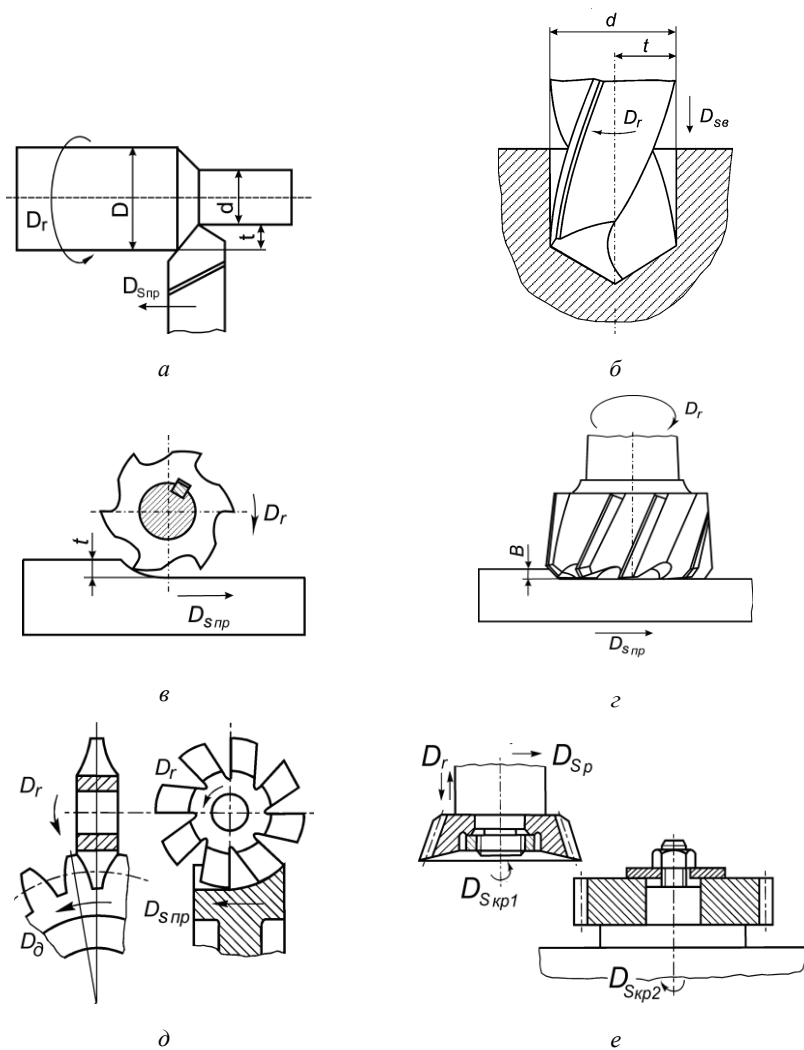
Виды главного движения и движения подач в токарных (*a*), сверлильных (*б*), фрезерных (*в-г*) и зубодолбежных (*е*) станках:
